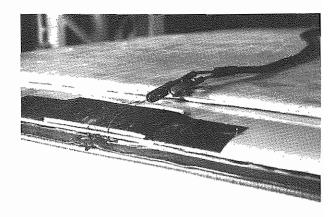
Collegere i cavi resistenza sigillante Connect sealing resistance cables
